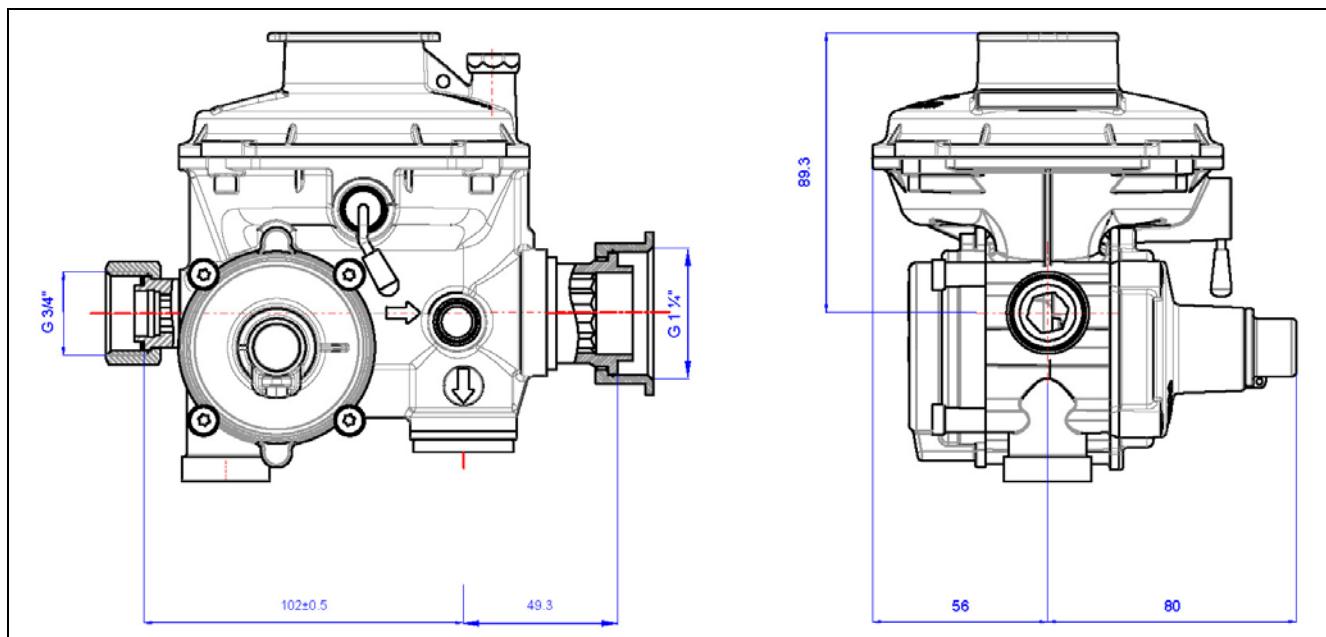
Габаритные и присоединительные размеры регулятора давления РД с линейным присоединением к трубопроводу
